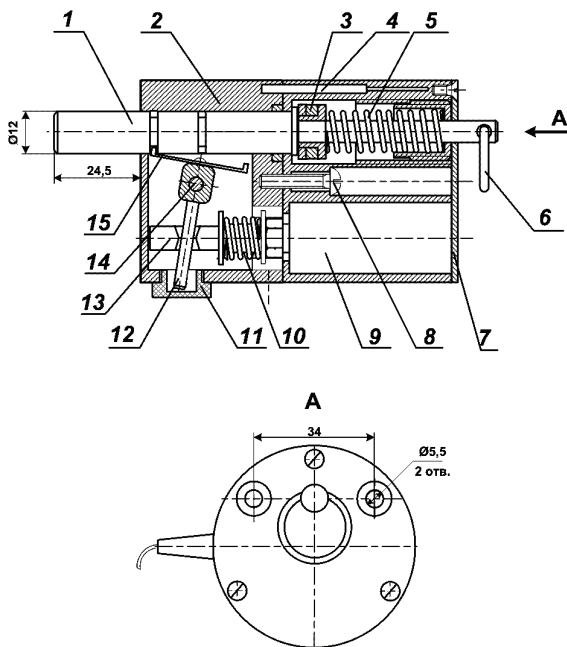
Кинематическая схема опытного образца УБОП: 1 – шток; 2 – корпус; 3 – кольцевой магнит; 4 – герконовое реле; 5 – возвратная пружина; 6 – кольцо; 7 – крышка; 8 – винт; 9 – электромагнит; 10 – пружина; 11 – пробка; 12 – рычаг; 13 – толкатель; 14 – ось; 15 – коромысло
